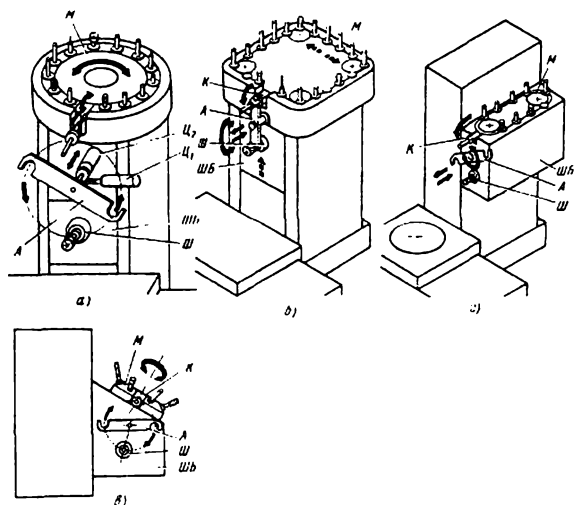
Компоновка механізмів МАЗІ при їх розташуванні:
